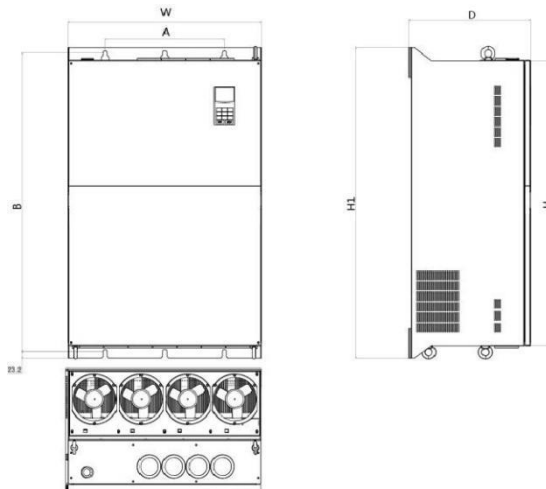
Diagrama esquemático de la dimensión externa y la dimensión de montaje de la estructura de placa metálica
